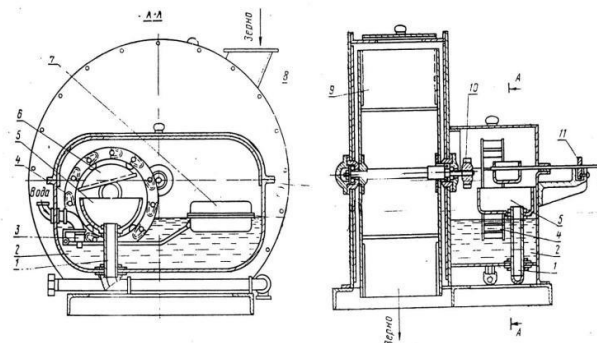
Водоструминна машина ЗЗМ-2: 1 – труба; 2 – резервуар; 3 – клапан; 4 – водоналивне колесо; 5 – воронка; 6 – лоток; 7 – поплавець; 8 – приймальний патрубков; 9 – лопатеве колесо; 10 – зубчата передача; 11 – гвинтовий регулятор кількості води.
